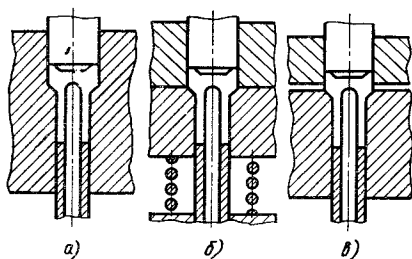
Схемы фасонирования дна полости и высадки фланца корпуса толкателя клапана (см. рис. 51, в):
